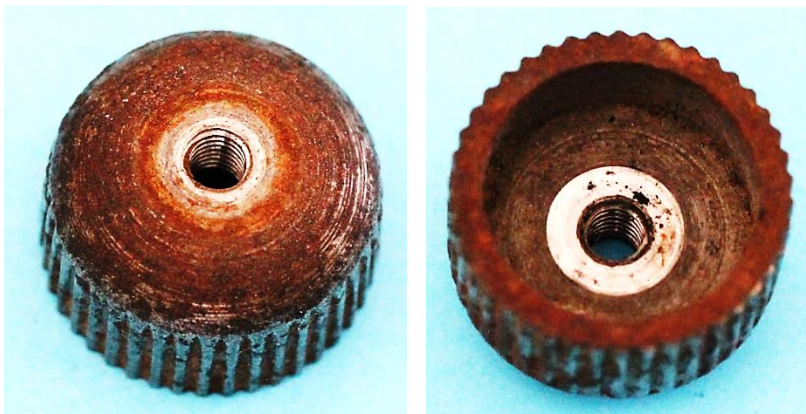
Stahlreibrad mit axialer Gewindebohrung
